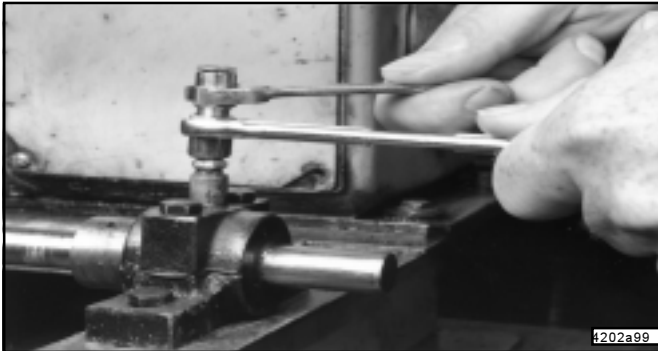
Serrer le raccord Quicklink dans le corps Zerk-Lock
